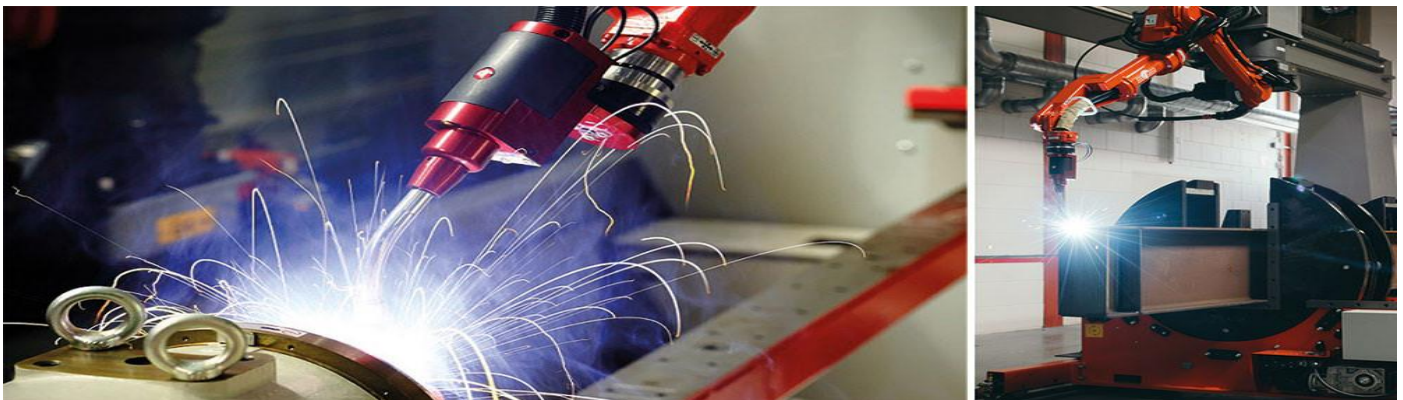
SOUDAGE MIG/MAG AUTOMATISÉ SUR ROBOT PROCÉDÉS 131-135
